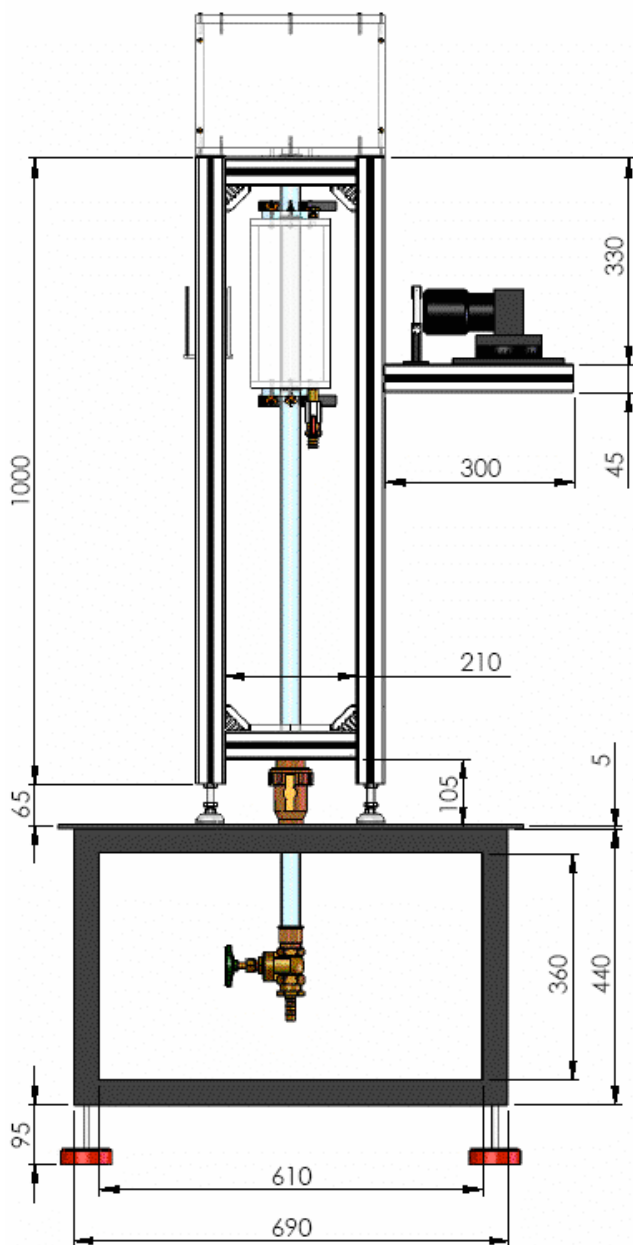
Desenho técnico da bancada experimental (vista frontal)
